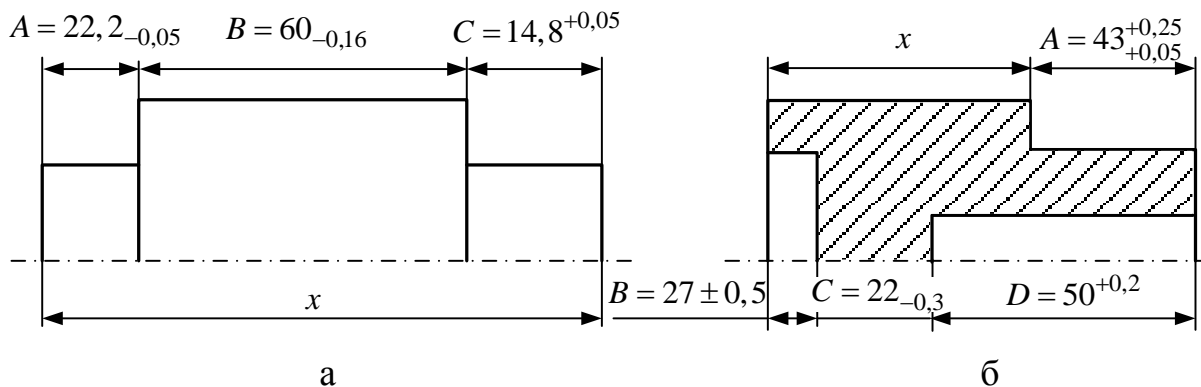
Размеры на чертежах деталей: а – вал; б – втулка
